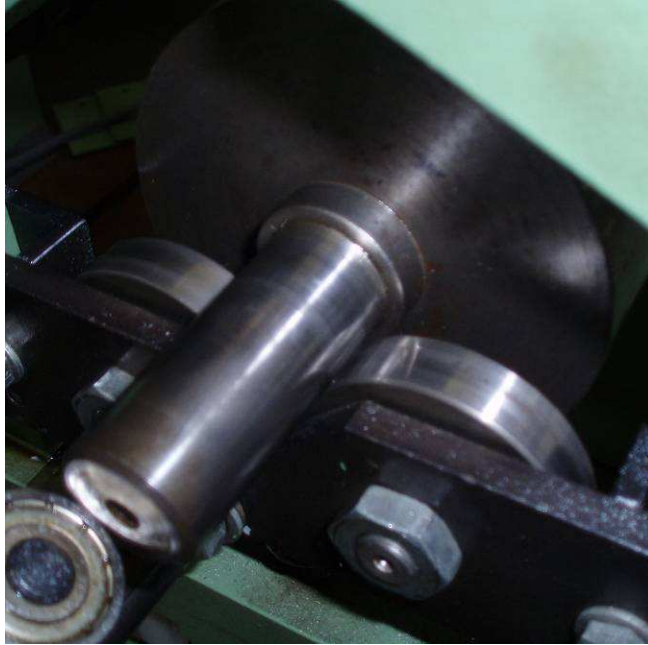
Montaje del eje en los rodillos del pedestal.
